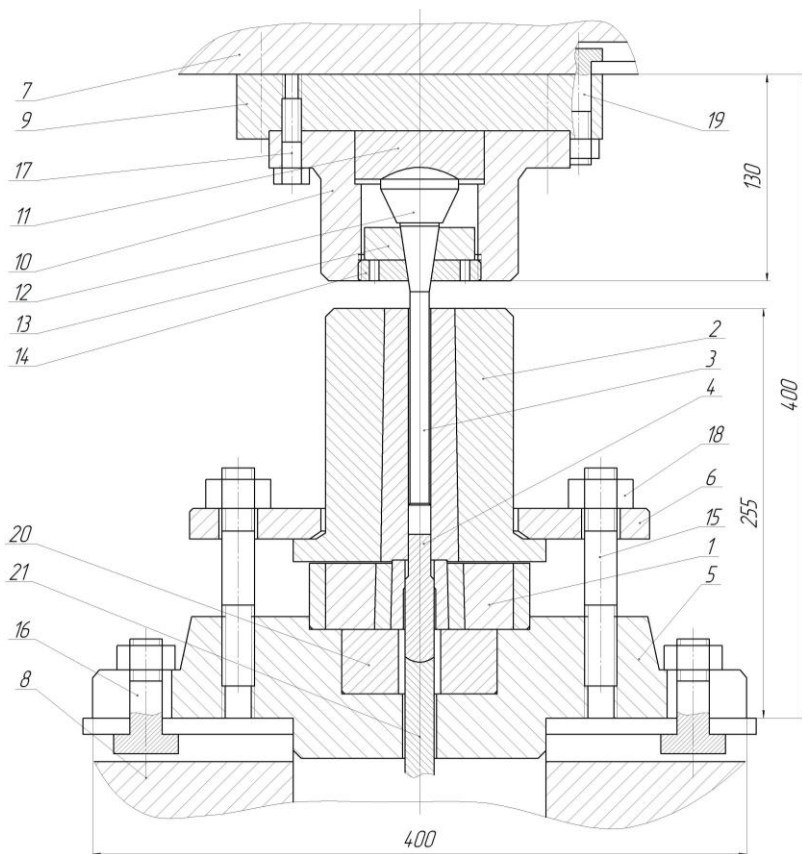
Загальний вигляд штамп для прямого видавлювання з роздачею профілів через призматичну матрицю з круглих заготовок
